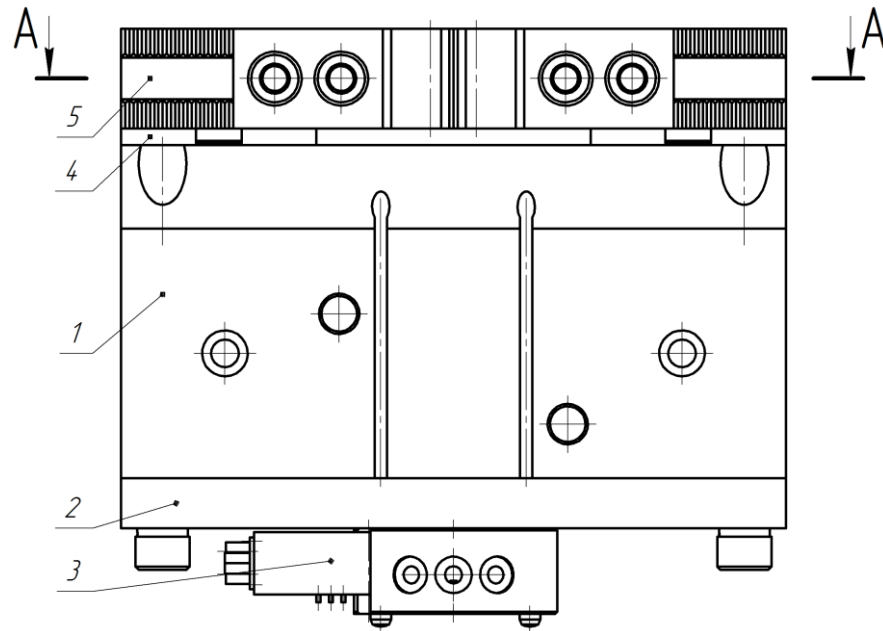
Захоплювальний пристрій для деталей типу вилки.
